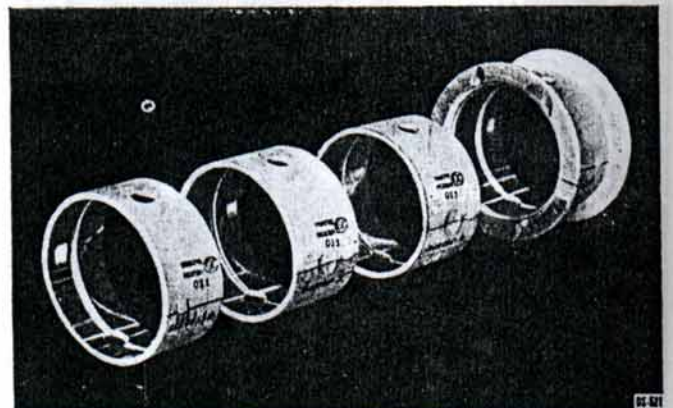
Conjunto cojinete de bancada para motores 6L-226.
